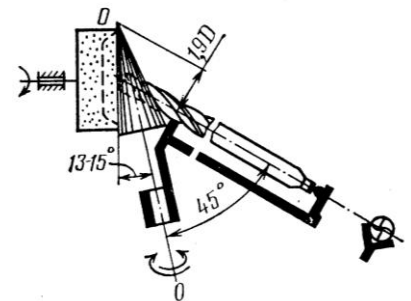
Схема конічного заточування задньої поверхні свердла
